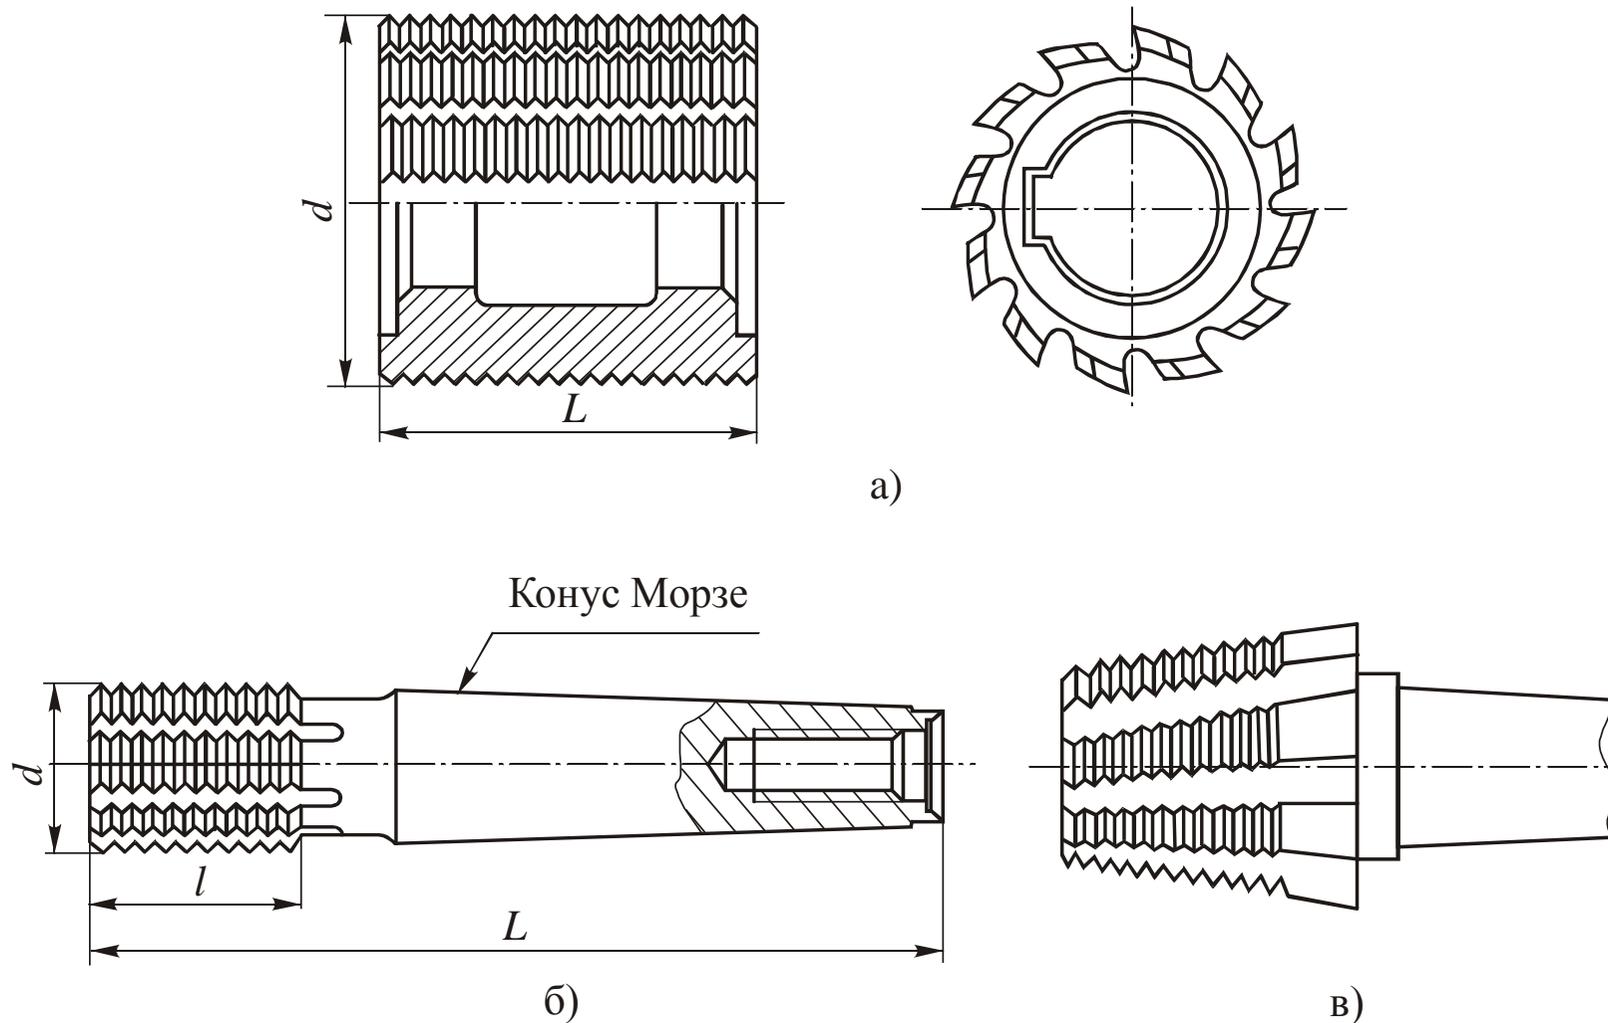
Гребенчатые резьбонарезные фрезы: *а* – цилиндрическая насадная; *б* – цилиндрическая концевая; *в* – для нарезания конических резьб
